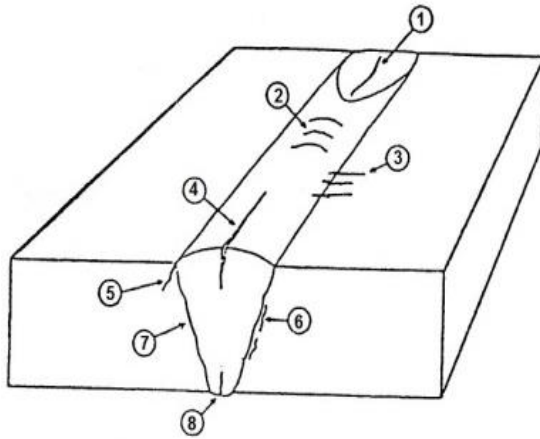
Posiciones de grietas en la soldadura [22].
